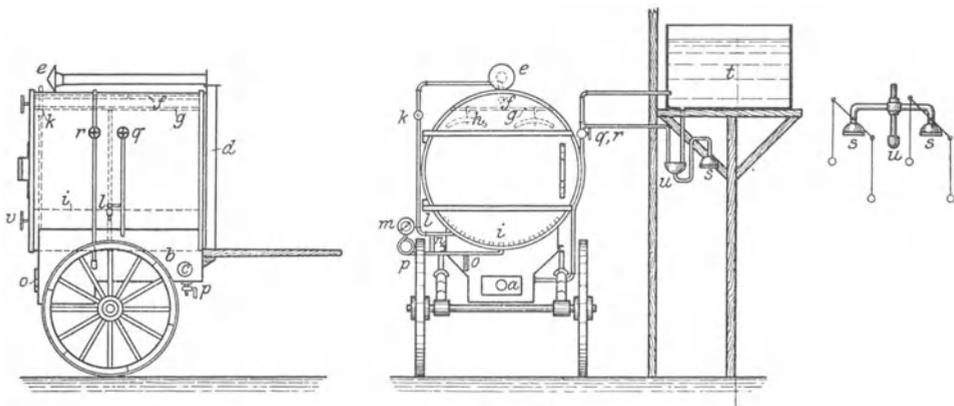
Dampfdesinfektionswagen mit Warmwasserdusche.
